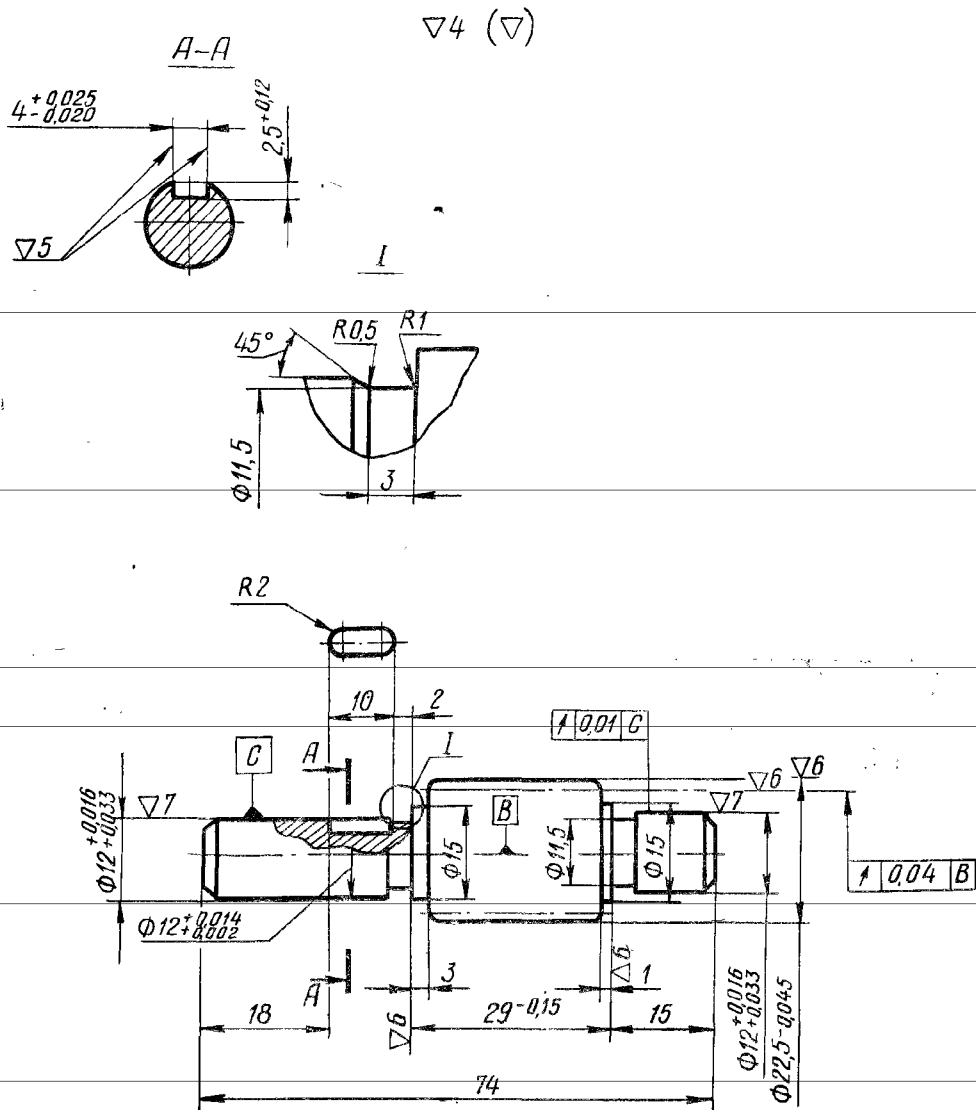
ВАЛИК-ШЕСТЕРНЯ 21 30
